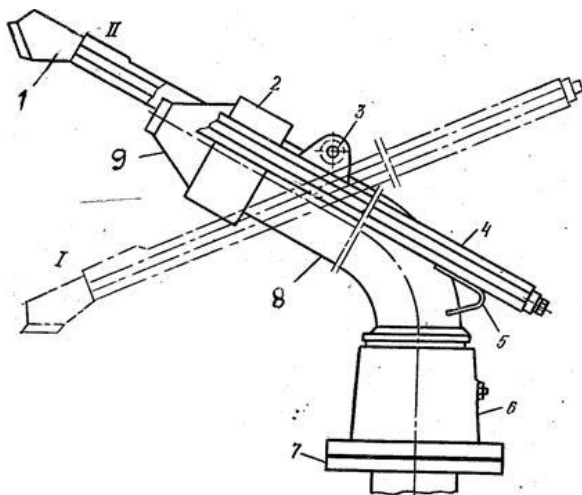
Дальнеструйный аппарат с качающимся коромыслом: I – коромысло при нижнем положении лопатки; II – коромысло при верхнем положении лопатки; 1 – лопатка; 2 – накидная гайка; 3 – ось качания; 4 – коромысло; 5 – противовес; 6 – корпус; 7 – присоединительный фланец; 8 – ствол; 9 – сопло.
